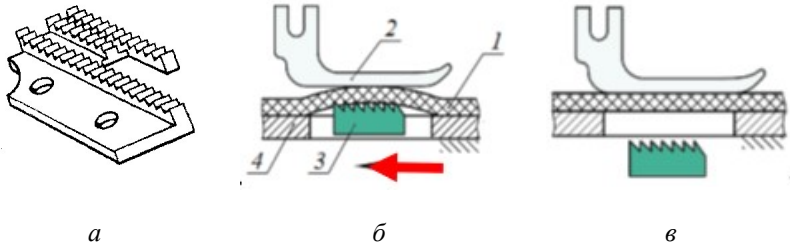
Схеми взаємодії зубчастої рейки з матеріалом: *а* – зубчата рейка; *б* – верхнє положення рейки при просуванні матеріалу «вперед»; *в* – нижнє положення рейки і «вистій» матеріалу; *1* – матеріал; *2* – притискна лапка; *3* – зубчата рейка; *4* – голкова пластина
